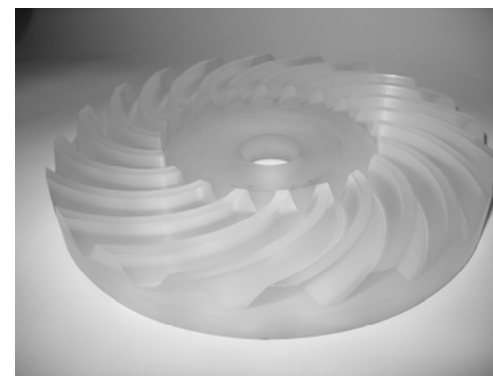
Прототип плоского конического колеса, изготовленный на станке с ЧПУ
